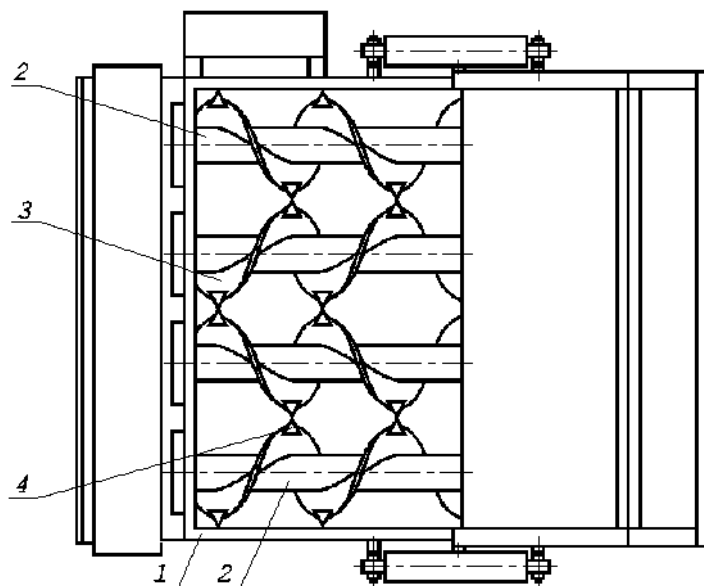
Перероблювальний шнековий пристрій з ріжучими елементами:
